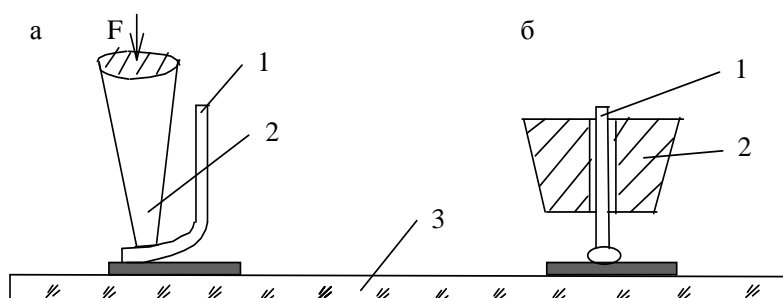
Схемы термокомпрессионной сварки:
